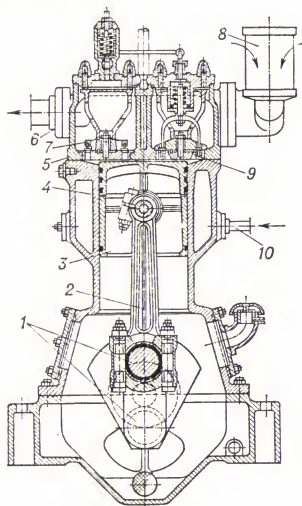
Поршневой компрессор: 1 — коленчатый вал; 2 — шатун; 3 — поршень; 4 — рабочий цилиндр; 5 — крышка цилиндра; 6 — нагнетательный трубопровод; 7 — нагнетательный клапан; 8 — воздухозаборник; 9 — всасывающий клапан; 10 — труба для подвода охлаждающей воды.
